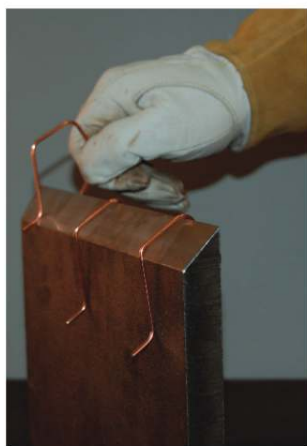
• Platzieren der Schweißspaltklammer auf dem Bauteil (alle Bilder: Palige Schweißtechnik, www.palige-schweisstechnik.de).
